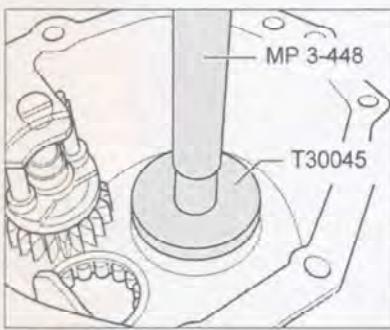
Установка наружной обоймы малого роликоподшипника.
